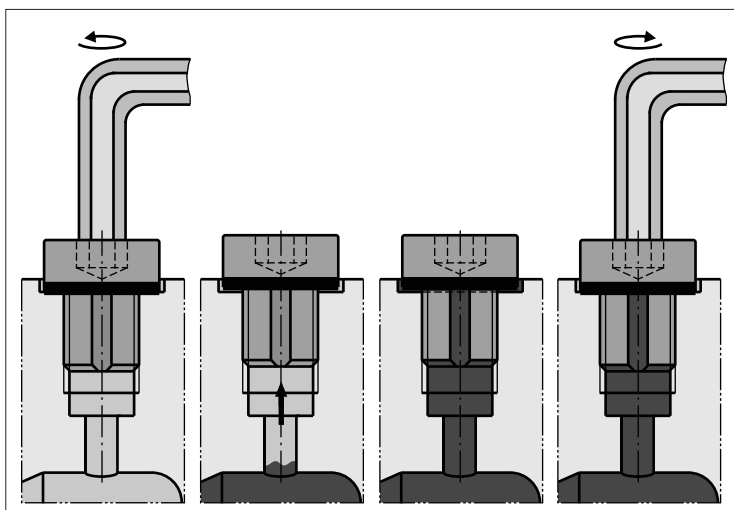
Hydraulikzylinder mit Innensechskant-Entlüftungsschraube befüllen und entlüften
